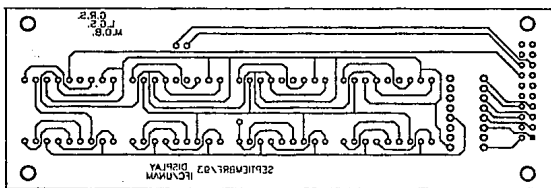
Cara de soldadura del circuito impreso de la etapa de desplegado.
